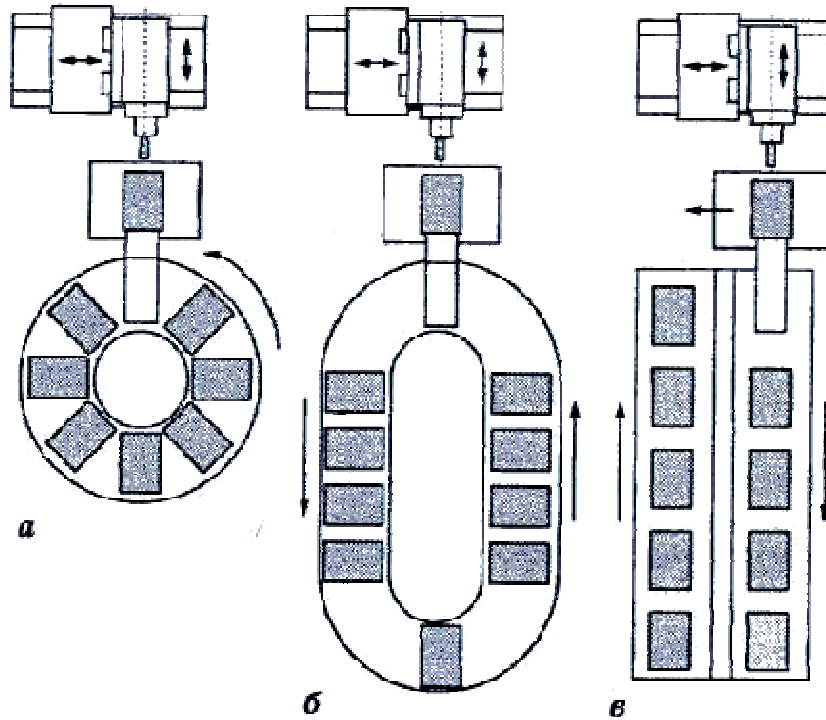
Подвижные магазины палет, используемые в ГПМ для обработки корпусов:
